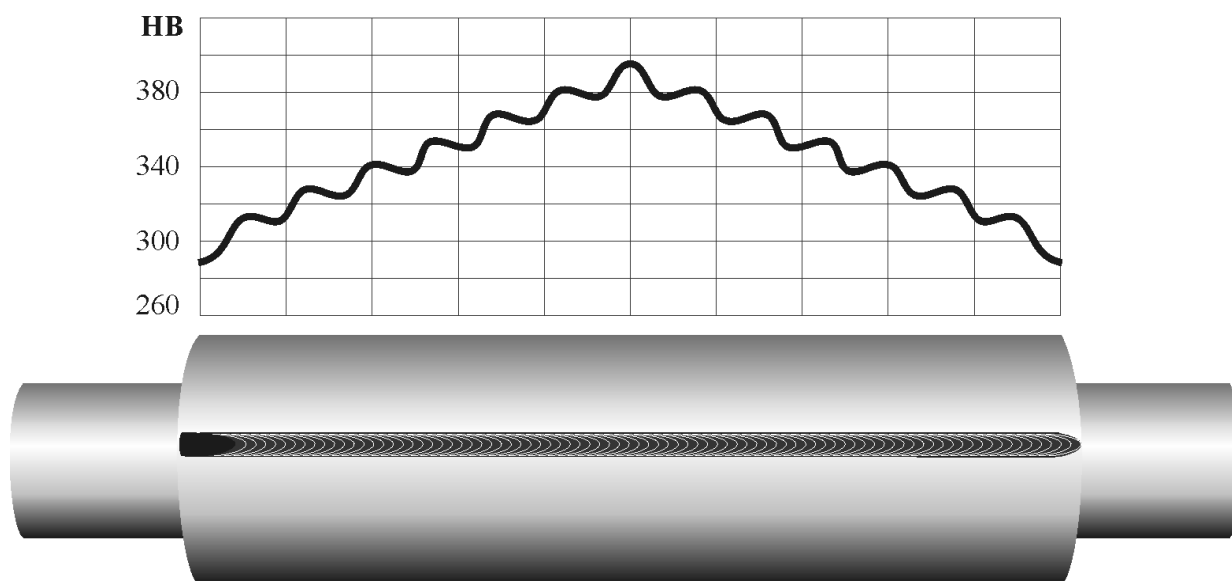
Схема розподілу твердості вздовж бочки прокатного валка при формуванні наплавленого шару з поздовжніх валиків.
